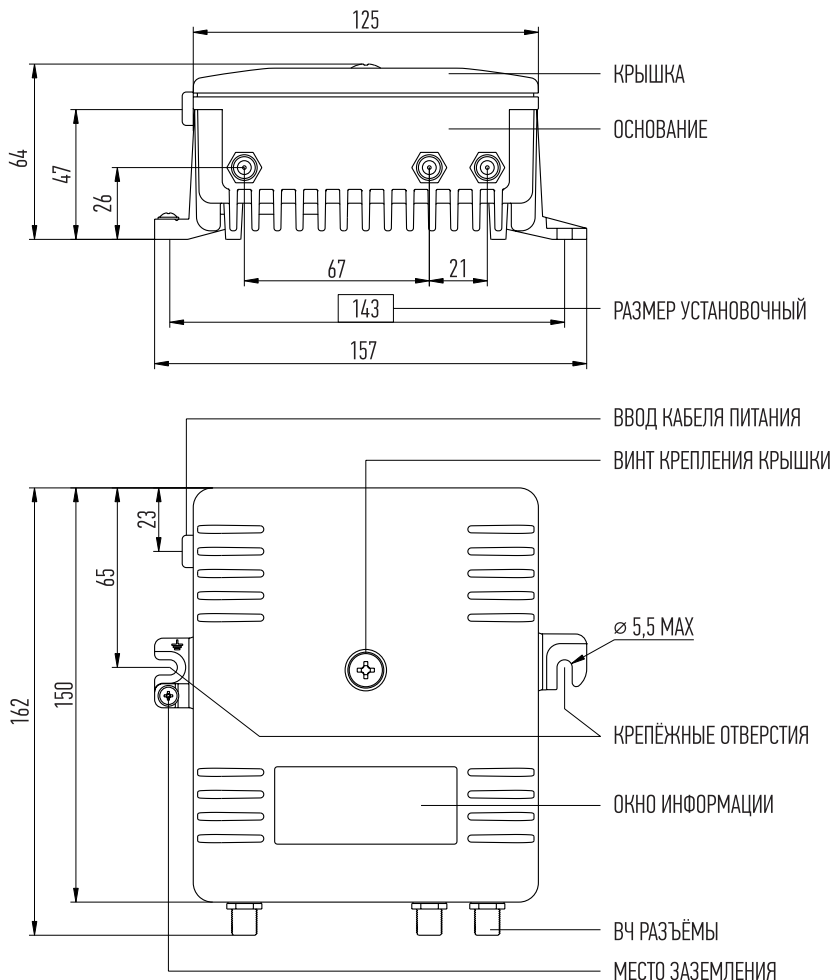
Габаритные и установочные размеры (в мм), основные компоненты корпуса
